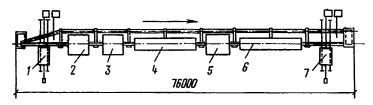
Схема конвейерной линии для окраски в электрополе (НИИЖБ — НПО Лакокраспокрытие — КБ по железобетону)
